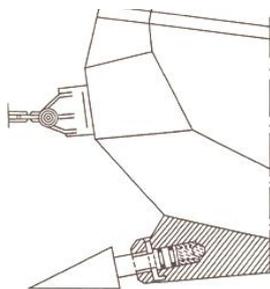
Ковш экскаватора с подвижными зубьями (а.с. № 616371 СССР)
